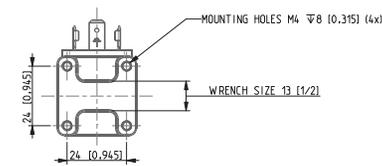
Dimensiones 1/8" en línea, ancho de bobina 32 mm
